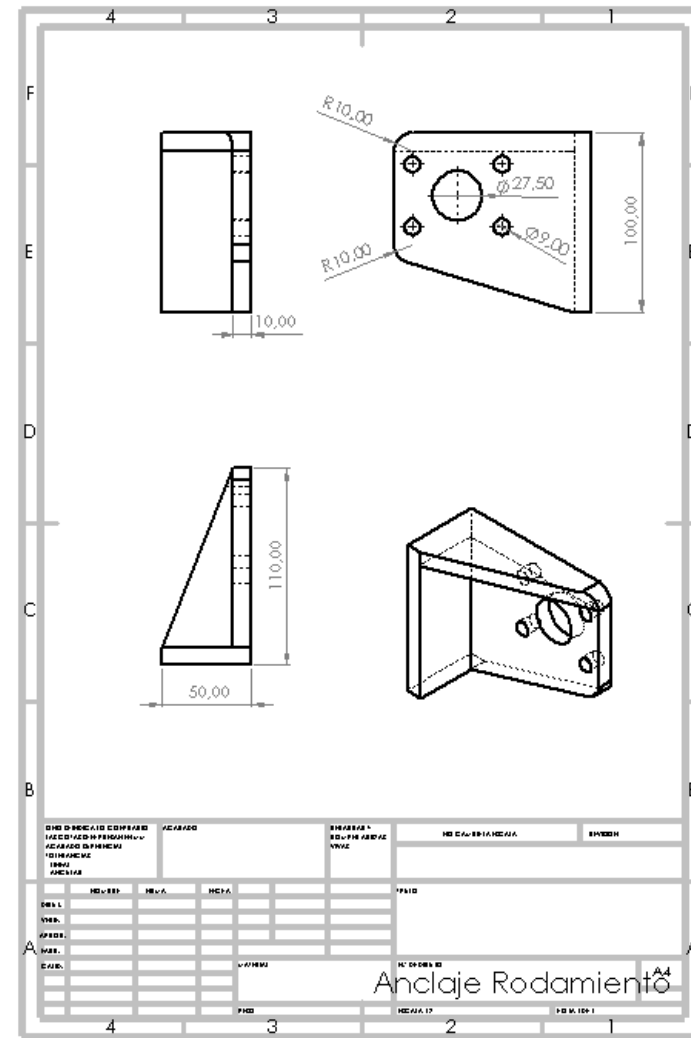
Soporte anclaje Motor Principal unión con ensamblaje rodamiento
